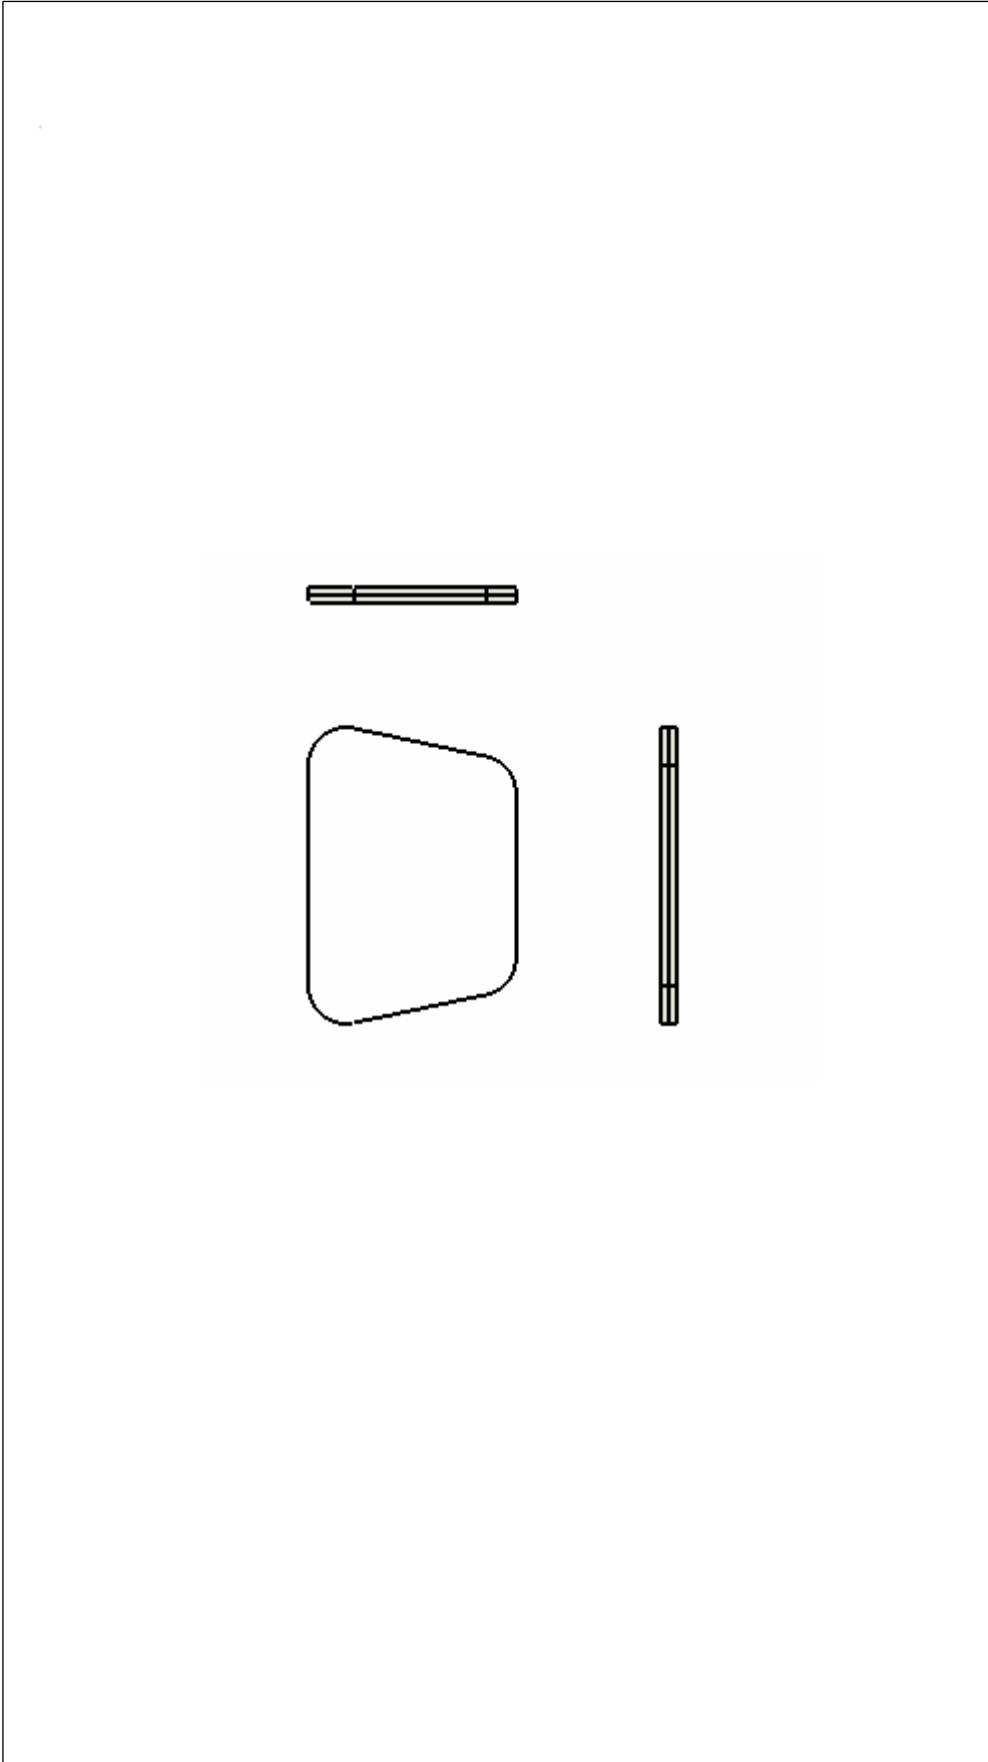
Drawing ชุดจับยึดหัวอ่าน-เขียน (Head Gimbal Assembly)
